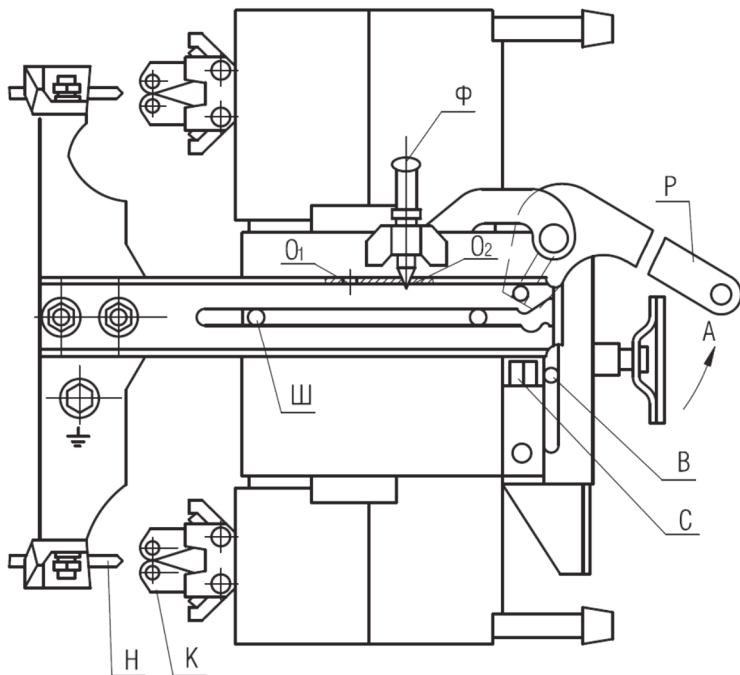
Выключатель выдвигного исполнения в положении разъединителя
